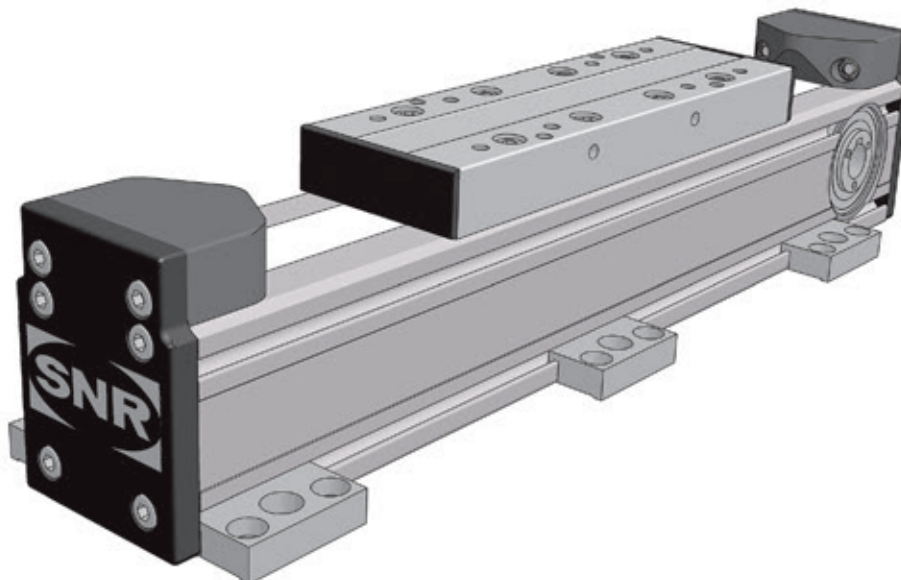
Linearachse AXC mit Befestigungsleisten
